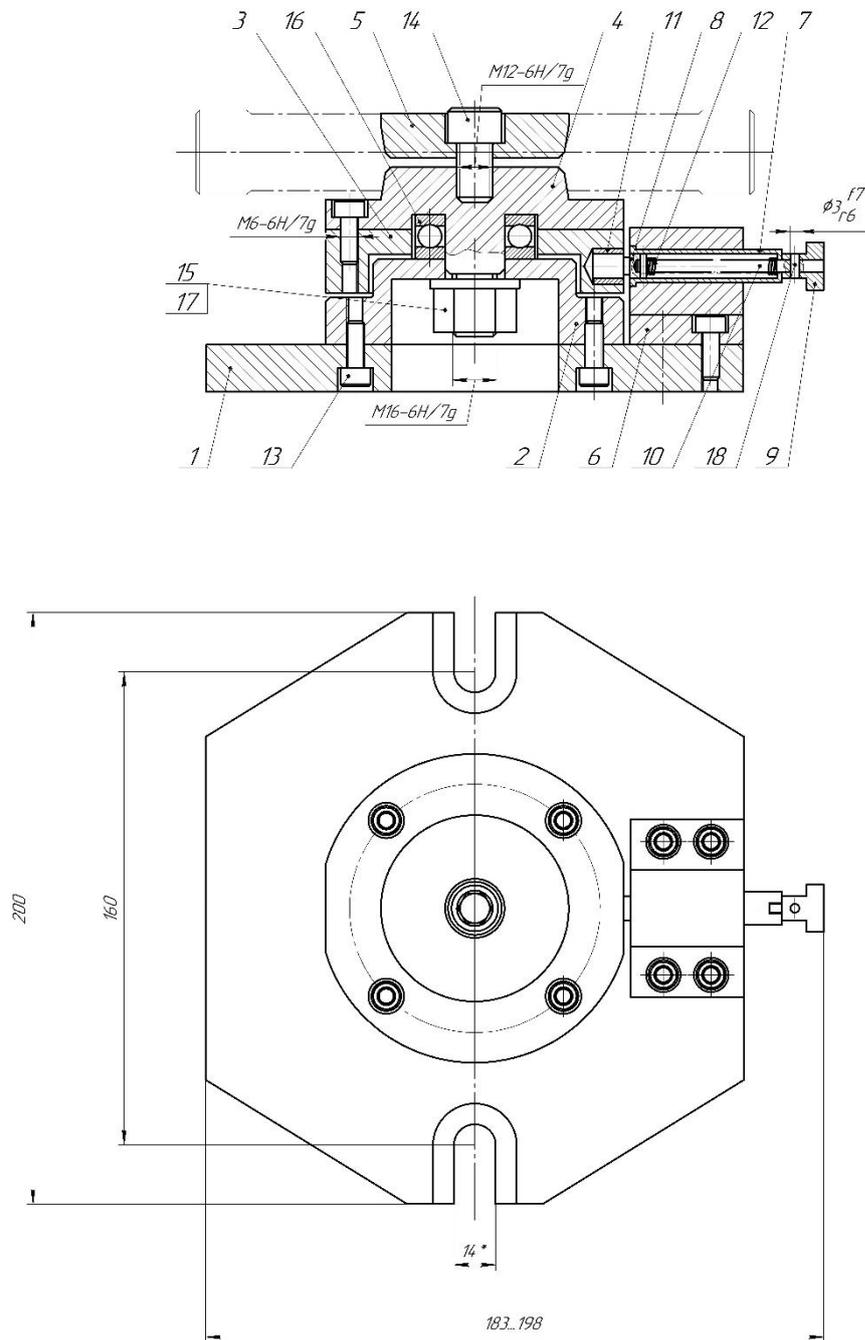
Пристрій для відновлення хрестовин: 1 – плита; 2 – корпус; 3 – стіл; 4 – підставка; 5 – шайба; 6 – корпус малий; 7 – корпус фіксатора; 8 – фіксатор; 9 – ручка; 10- стріжень; 11 – втулка; 12 – пружина.
